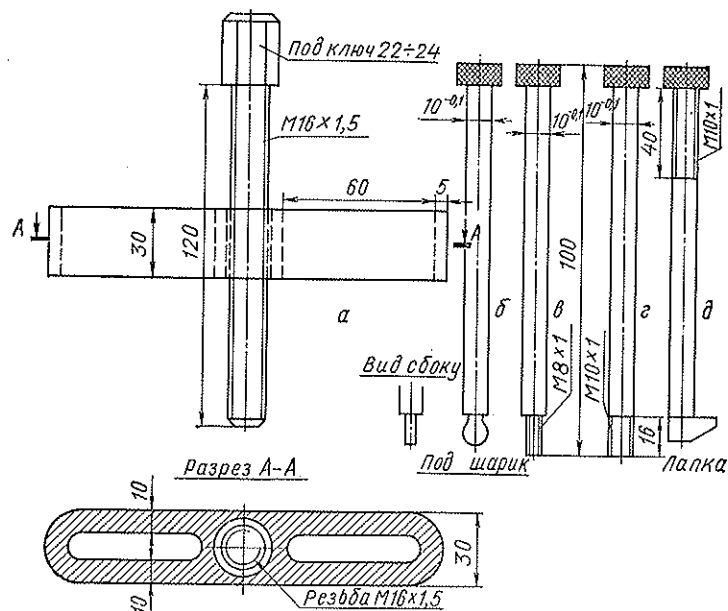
Универсальный съемник с комплектом приспособлений: а — съемник; б — приспособление для выпрессовки подшипников; в — болты для снятия задней крышки; г — болты для снятия маховика; д — лопки для снятия шестерен.
